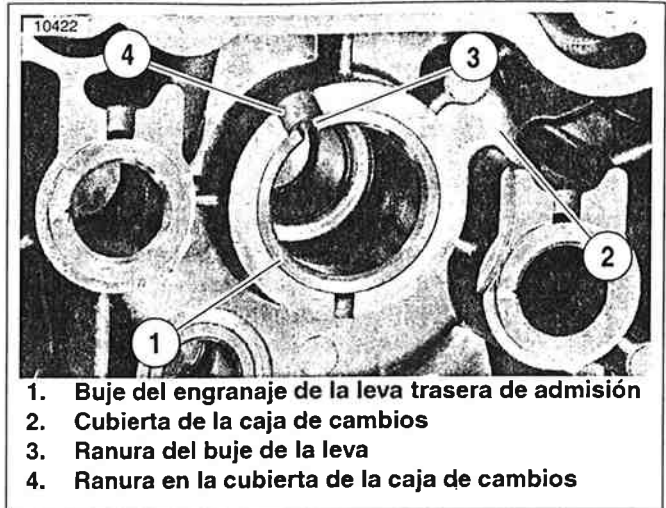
Buje trasero del engranaje de la leva de admisión instalado en la cubierta de la caja de cambios
